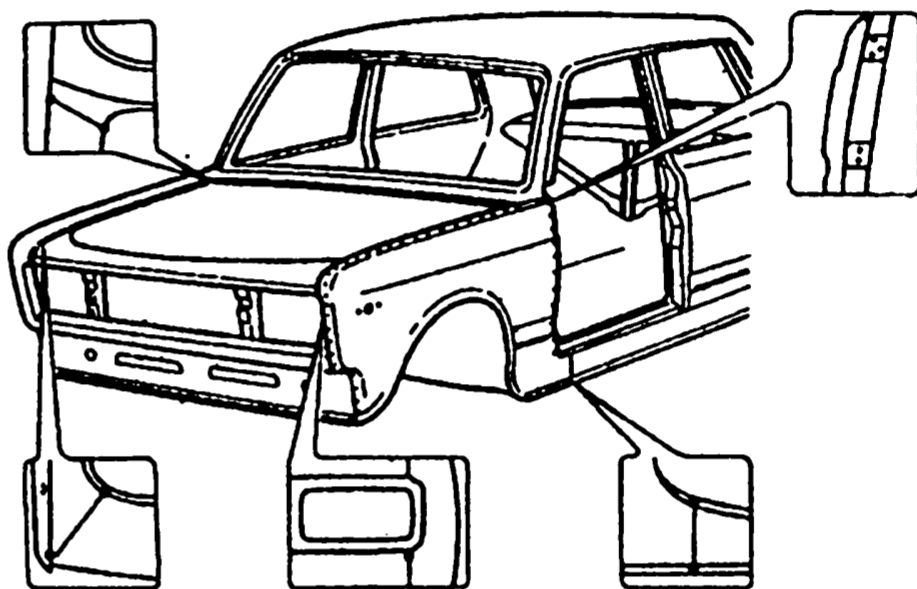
Места сварки переднего крыла. На основном виде точками обозначены швы контактной сварки. На фрагментах показаны точки газовой сварки
